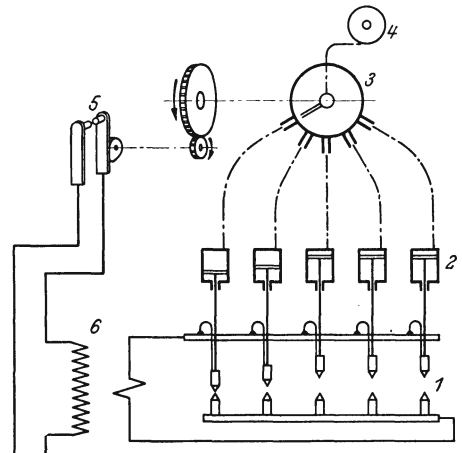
Aufbau einer Punktschweißmaschine mit Folgeelektroden.
